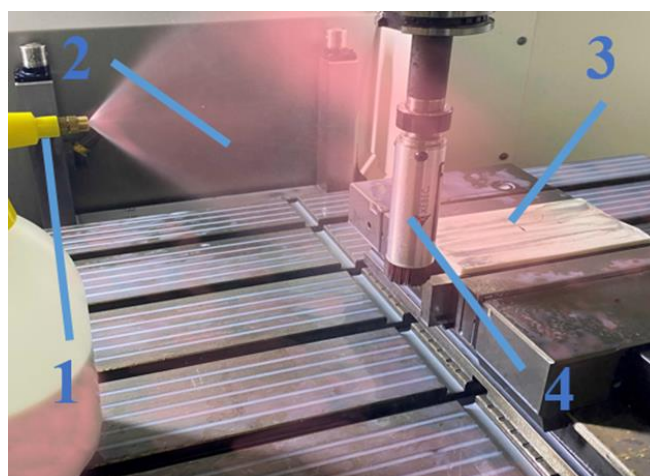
Эксперимент в насыщенном облаке СОЖ; 1 - Установка распыления СОЖ, 2 - Облако СОЖ, 3 - Заготовка, 4 - Абразивная щётка
